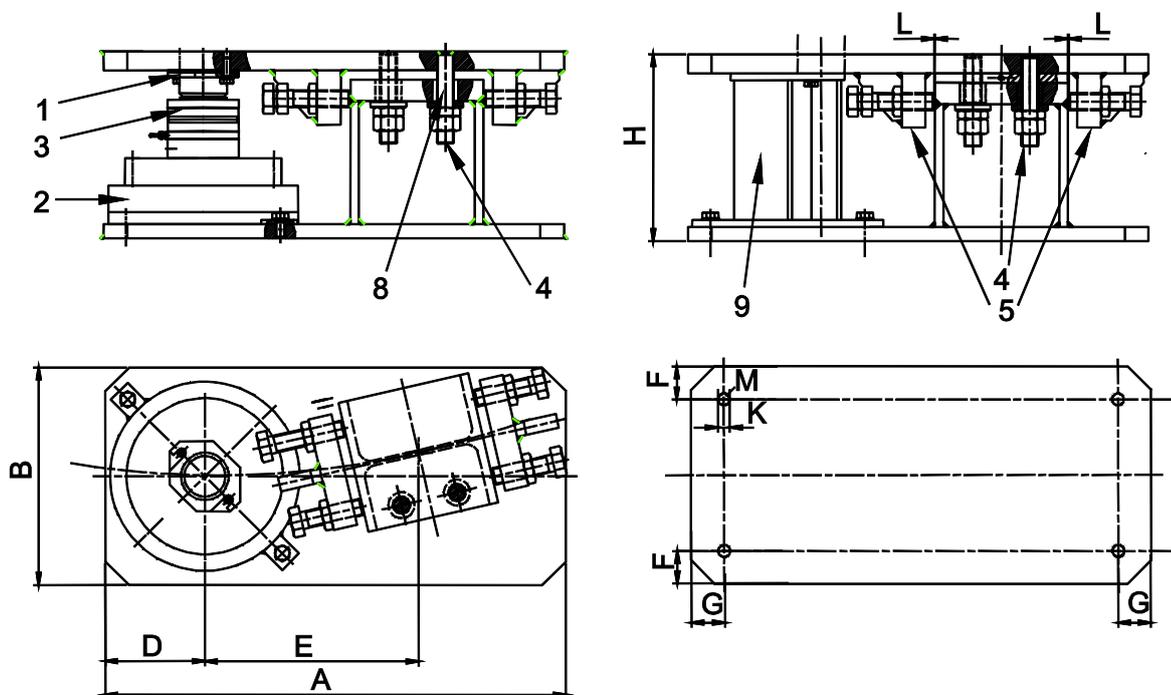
Einbauzeichnung Kompaktlager VKN-Lager 47 ... 470 t
